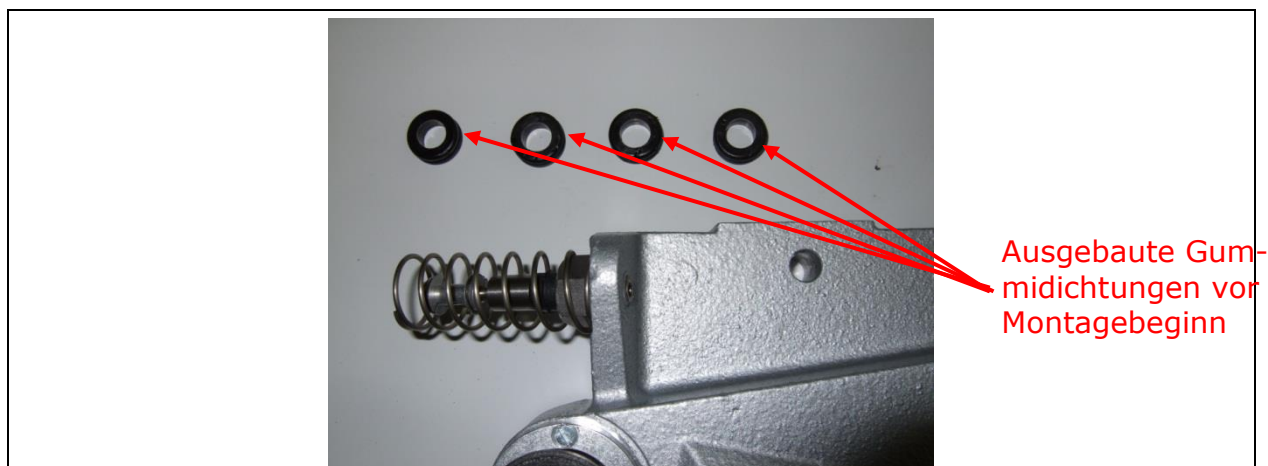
Schritt 5 Dichtungen vor Montage der Trägerplatte abziehen.
